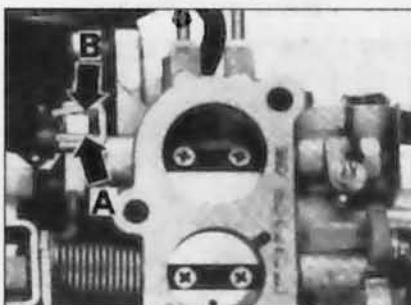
Зазор стопорного рычага карбюратора 2E2 с закрытыми дроссельными клапанами (Глава 11)
